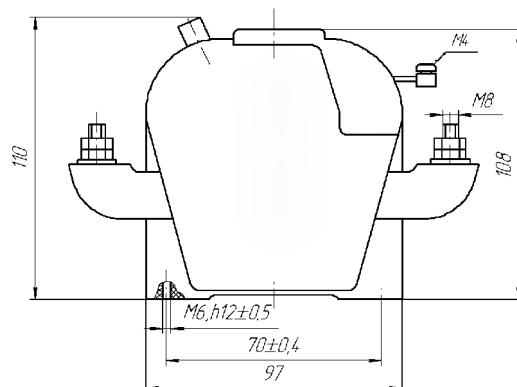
Габаритные, установочные и присоединительные размеры реле типа ТРТП-140.
